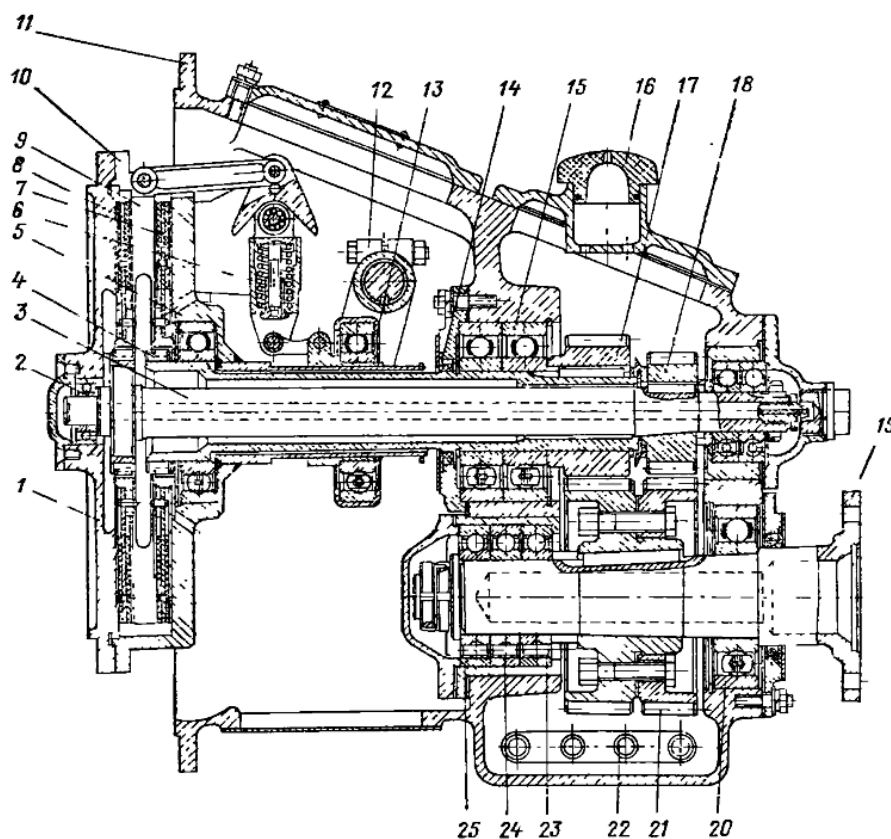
Поздовжній переріз реверс-редуктора РРП-20
